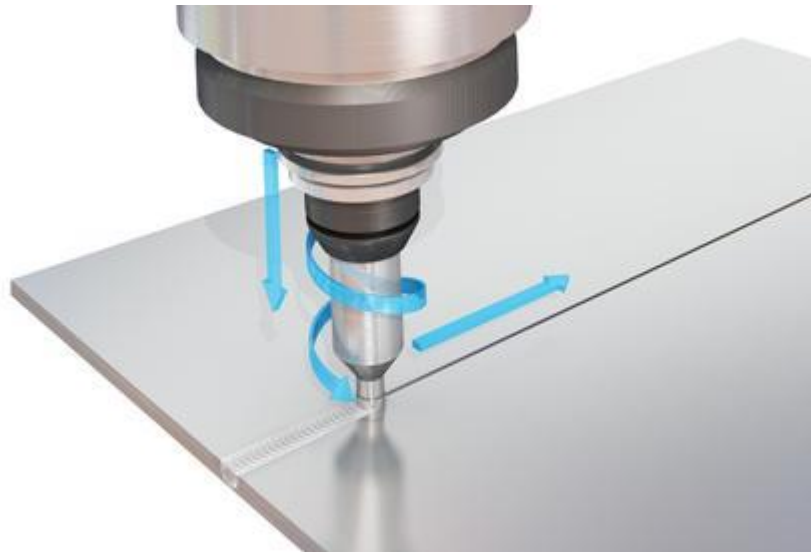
Soldadura FSW de duas chapas metálicas em configuração "Butt Joint" de junta retilínea – em <https://za.pinterest.com/pin/408912841142585093/>.
